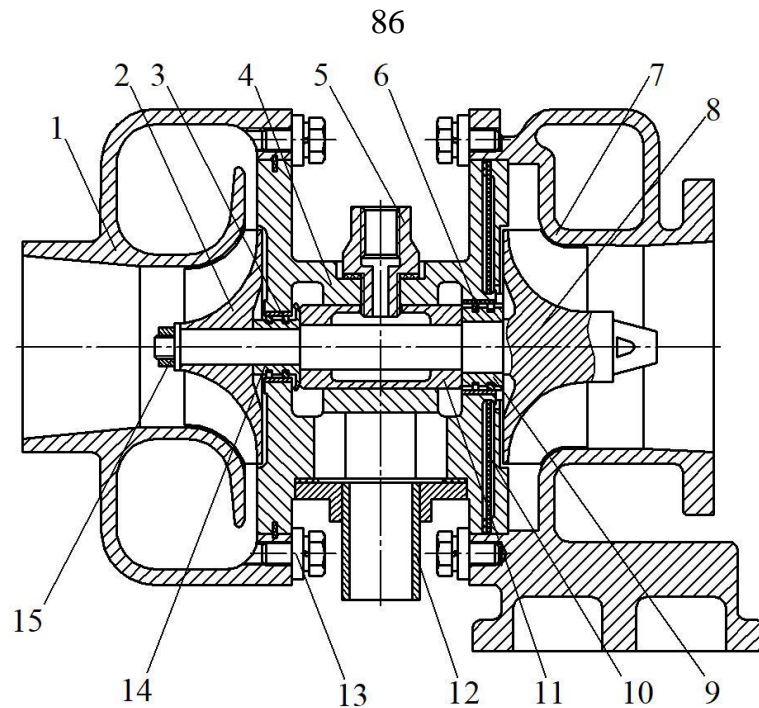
Продольный разрез турбокомпрессора ТКР6: 1 – корпус компрессора; 2 – колесо компрессора; 3 – кольцо уплотнения компрессора; 4 – корпус подшипника; 5 – штуцер подвода масла; 6 – кольцо уплотнения турбины; 7 – корпус турбины; 8 – колесо турбины; 9 – втулка уплотнения турбины; 10 – экран уплотнения; 11 – втулка подшипника; 12 – штуцер отвода масла; 13 – крепежная планка; 14 – втулка уплотнения колеса компрессора; 15 – гайка колеса
